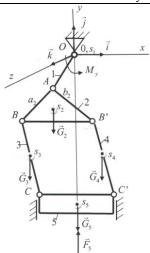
Рычажный механизма 4-го класса кривошипного пресса
